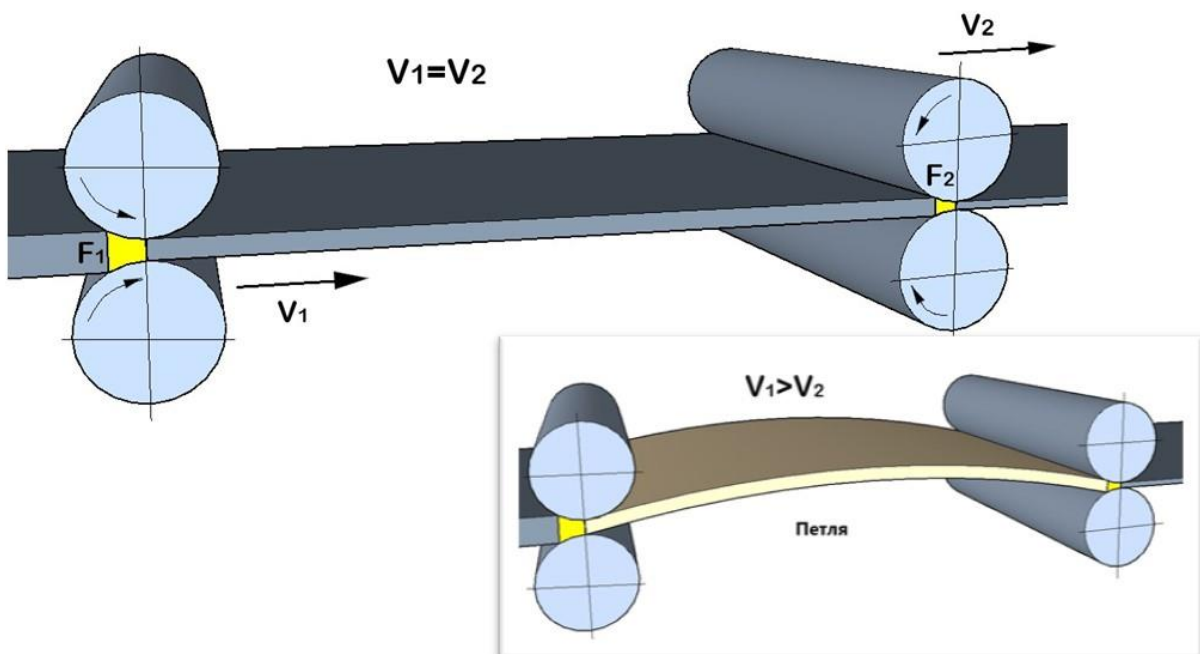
Схема одночасної прокатки заготовки у двох робочих клітях
